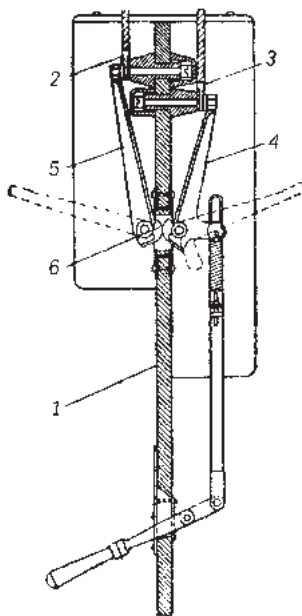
9 Выключатель Першаля с двойным разрывом цепи тока (1898 г.)
